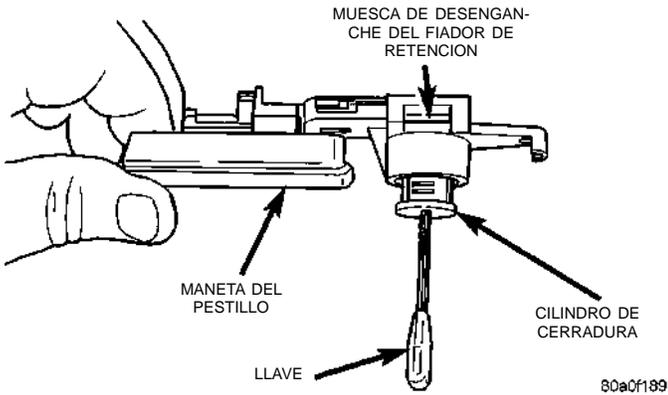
Desmontaje/instalación del cilindro de cerradura de la guantera
